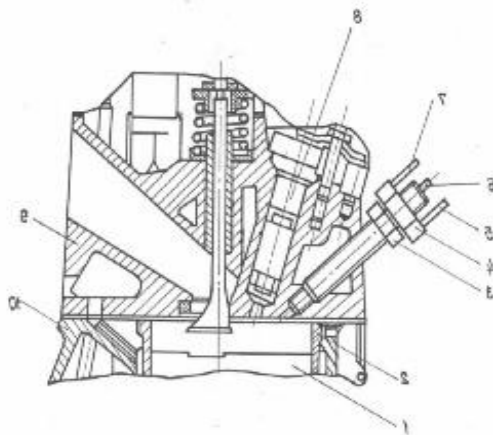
Схема установки пьезокварцевого датчика на двигателе КамАЗ-7403:1-поршень; 2-гильза; 3-стакан; 4-пьезодатчик; 5, 7-трубки подвода и отвода воды; 6-изолированный провод; 8-форсунка; 9-головка цилиндра; 10-блок цилиндров.
